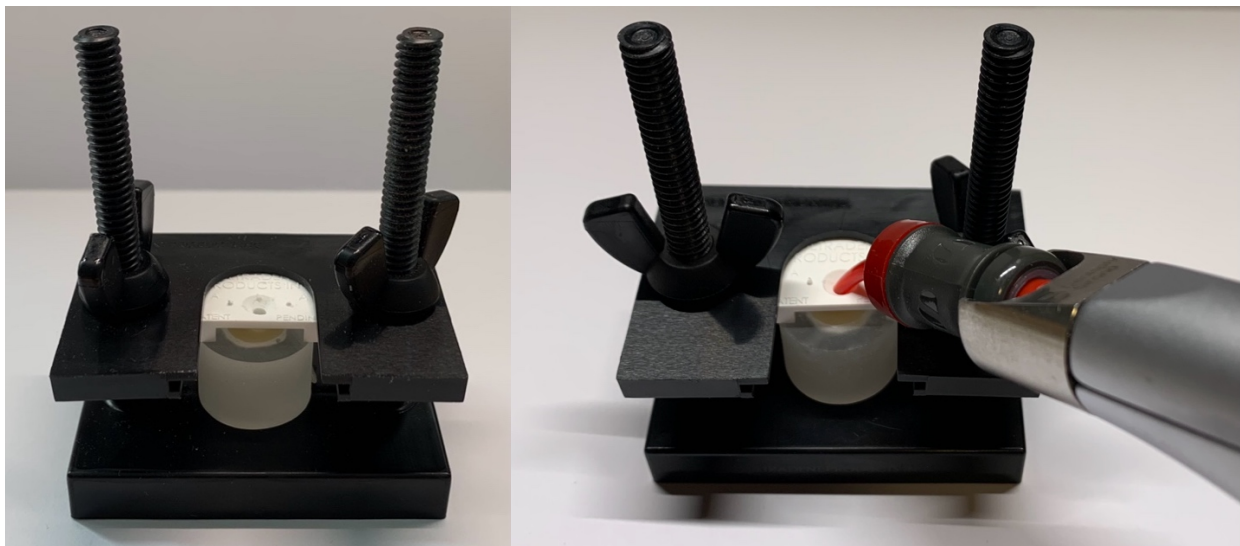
links: Bonding Clamp und Bonding Mold Inserts; rechts: Einbringen der Reparaturfüllung
